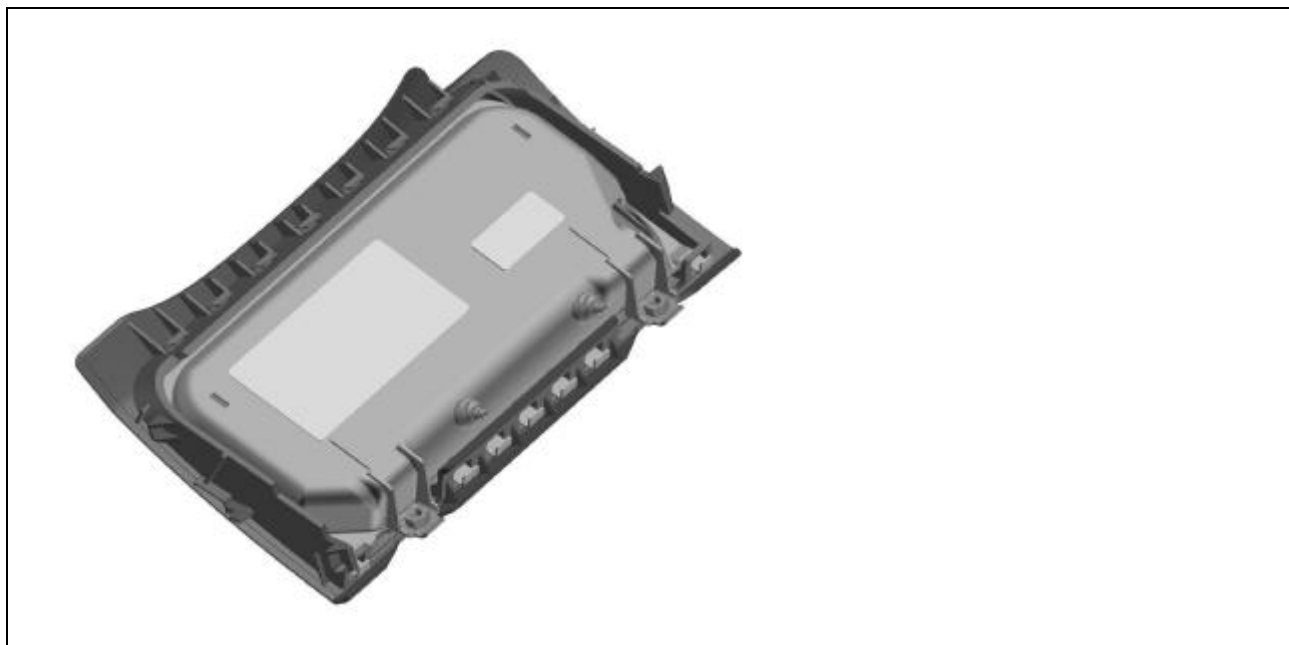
Bolsa de aire protectora de rodillas del conductor (detrás del protector de rodillas)
